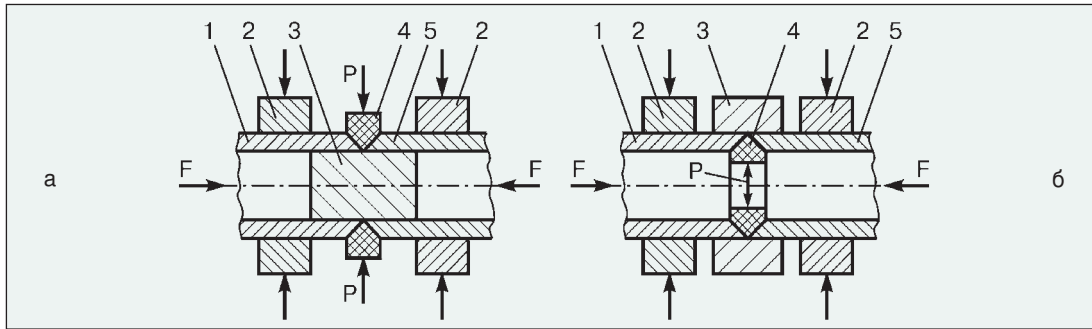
Схема радиальной сварки трением: а — с наружным разжимным кольцом; б — с внутренним (1 — маховик; 2, 3 — свариваемые заготовки; 4 — зажимной элемент; 5 — оправка)
